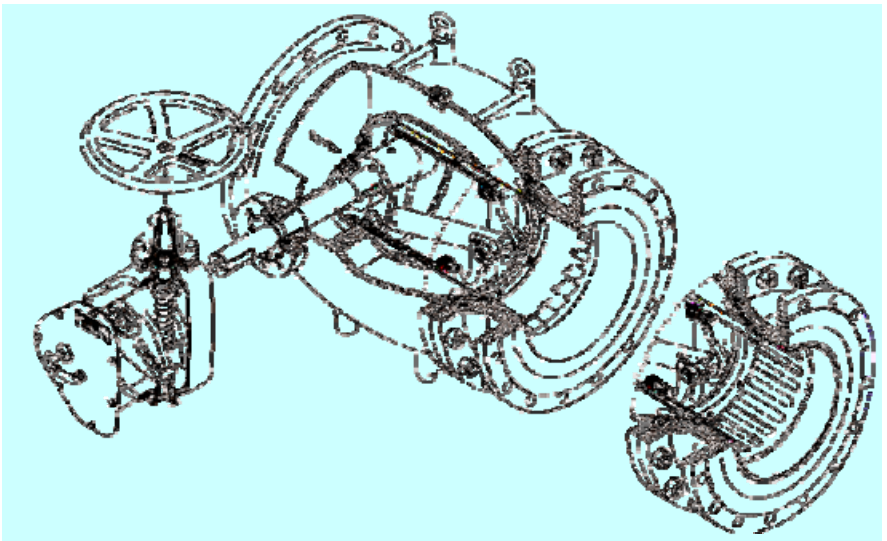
Secțiune printr-o vană inelară echipată cu cilindru cu fante sau cu inel cu palete
